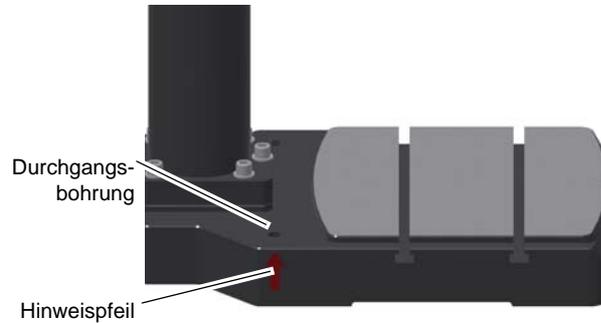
Kennzeichnung der Befestigungspunkte B34H
